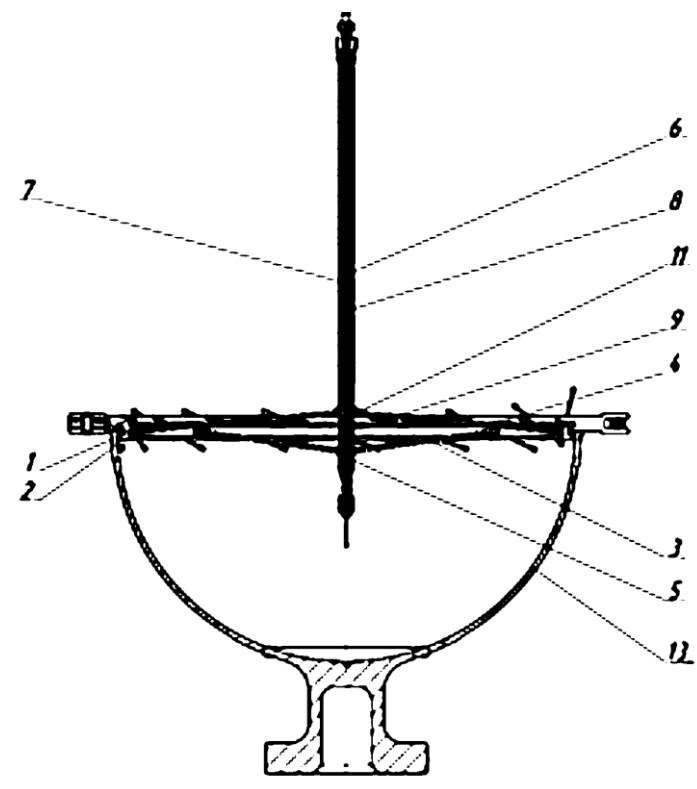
Конструкция приспособления для сборки шаровых баллонов.
